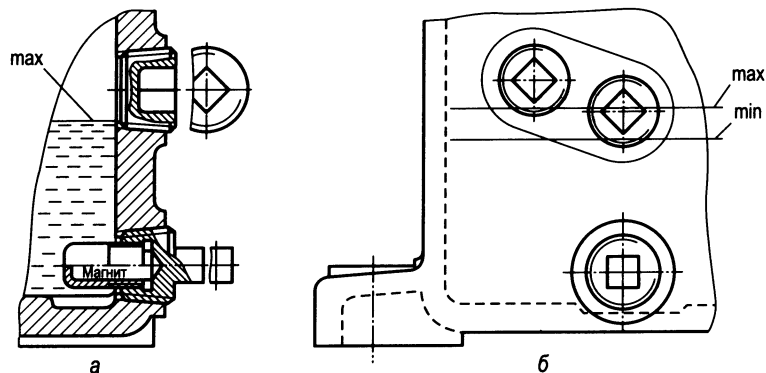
Маслоуказатели пробочные с одной (а) и двумя (б) коническими пробками
